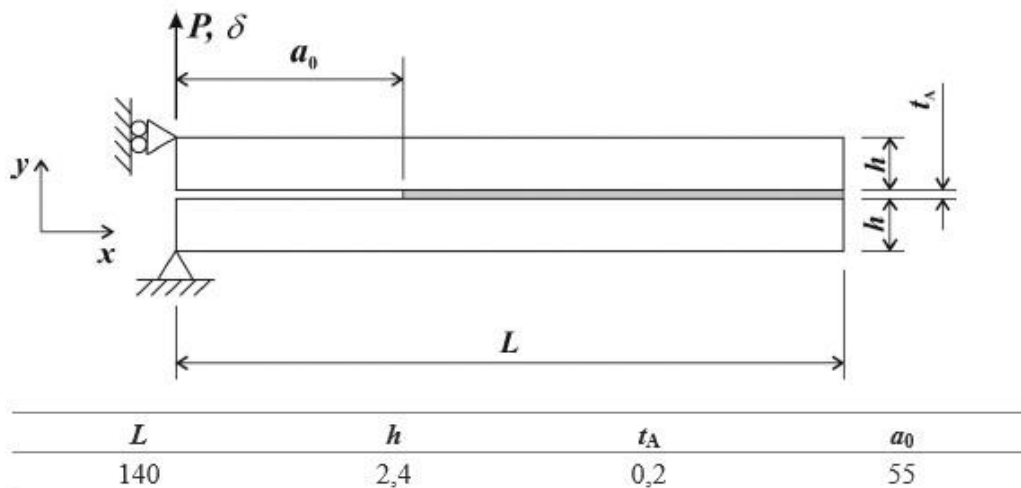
Configuração e dimensões das juntas do ensaio DCB (em mm) [50].
